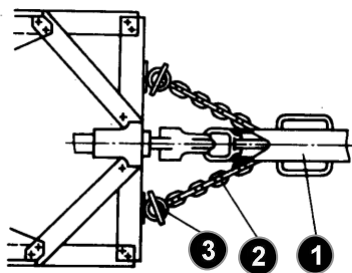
Схема крепления компрессорной станции предохранительными цепями
